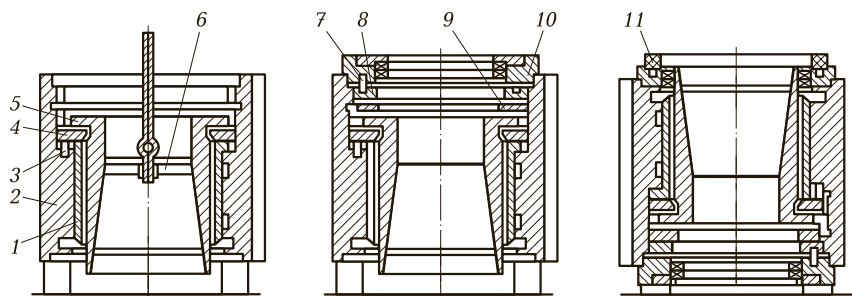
Схема сборки подшипника жидкостного трения:
